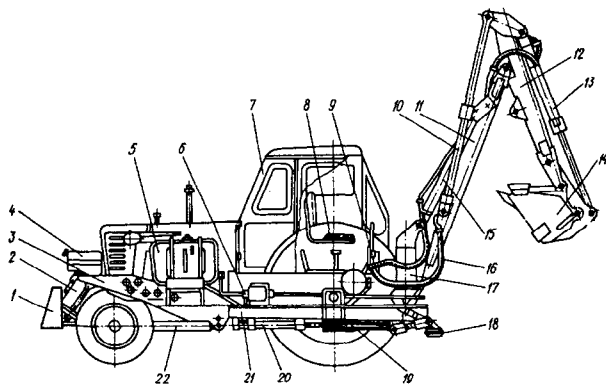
Общий вид одноковшового экскаватора: 1 – отвал; 2 – гидроцилиндр подъема отвала; 3 – рама; 4 – бак топливный; 5 – гидробак; 6 – рама; 7 – кабина; 8 – сиденье; 9 – шланги; 10 – гидроцилиндр рукояти; 11 – стрела; 12 – рукоять; 13 – гидроцилиндр ковш; 14 – ковш; 15 – гидроцилиндр стрелы; 16 – гидрошланг; 17 – стойка; 18 – аутригер; 19 – рама; 20 – кардан; 21,22 – рамы
